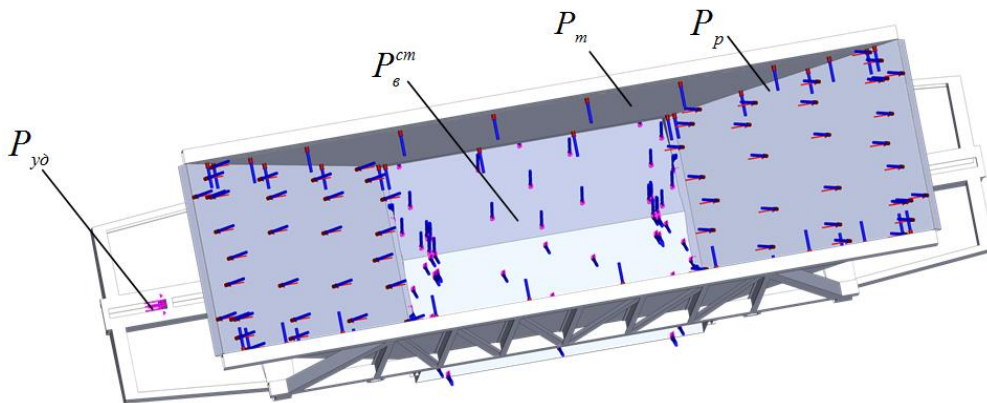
Розрахункова схема несучої конструкції вагона-хопера
